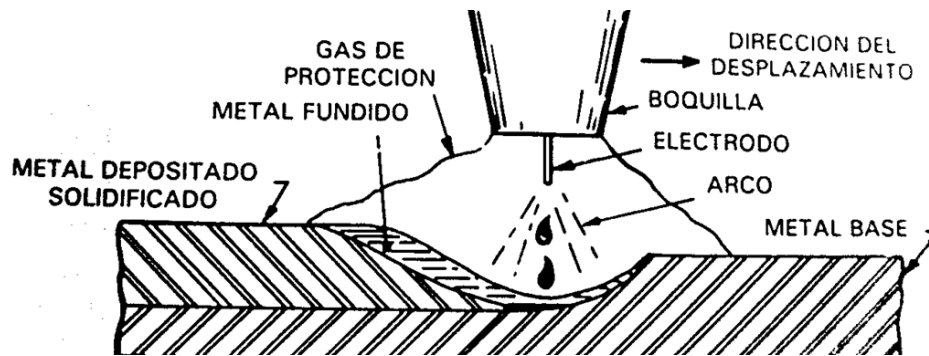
Proceso de soldadura por arco con alambre continuo protegido por gas (GMAW)
